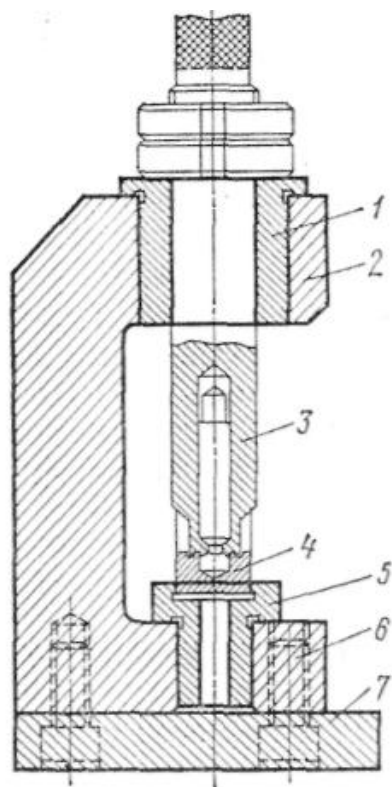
Приспособление для завальцовки поршня на штоке с помощью оправки:
